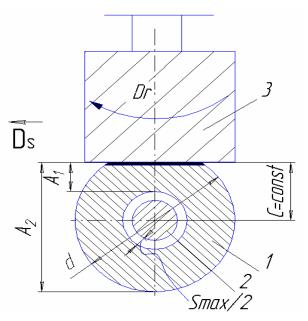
Базирование обрабатываемой заготовки на оправке с зазором
